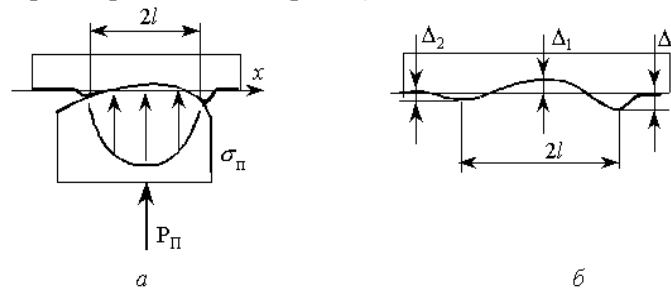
Схема взаємодії ролика з поверхнею заготовки (а) і вимірjana форма лунки на поверхні заготовки при повороті деталі на один оберт
